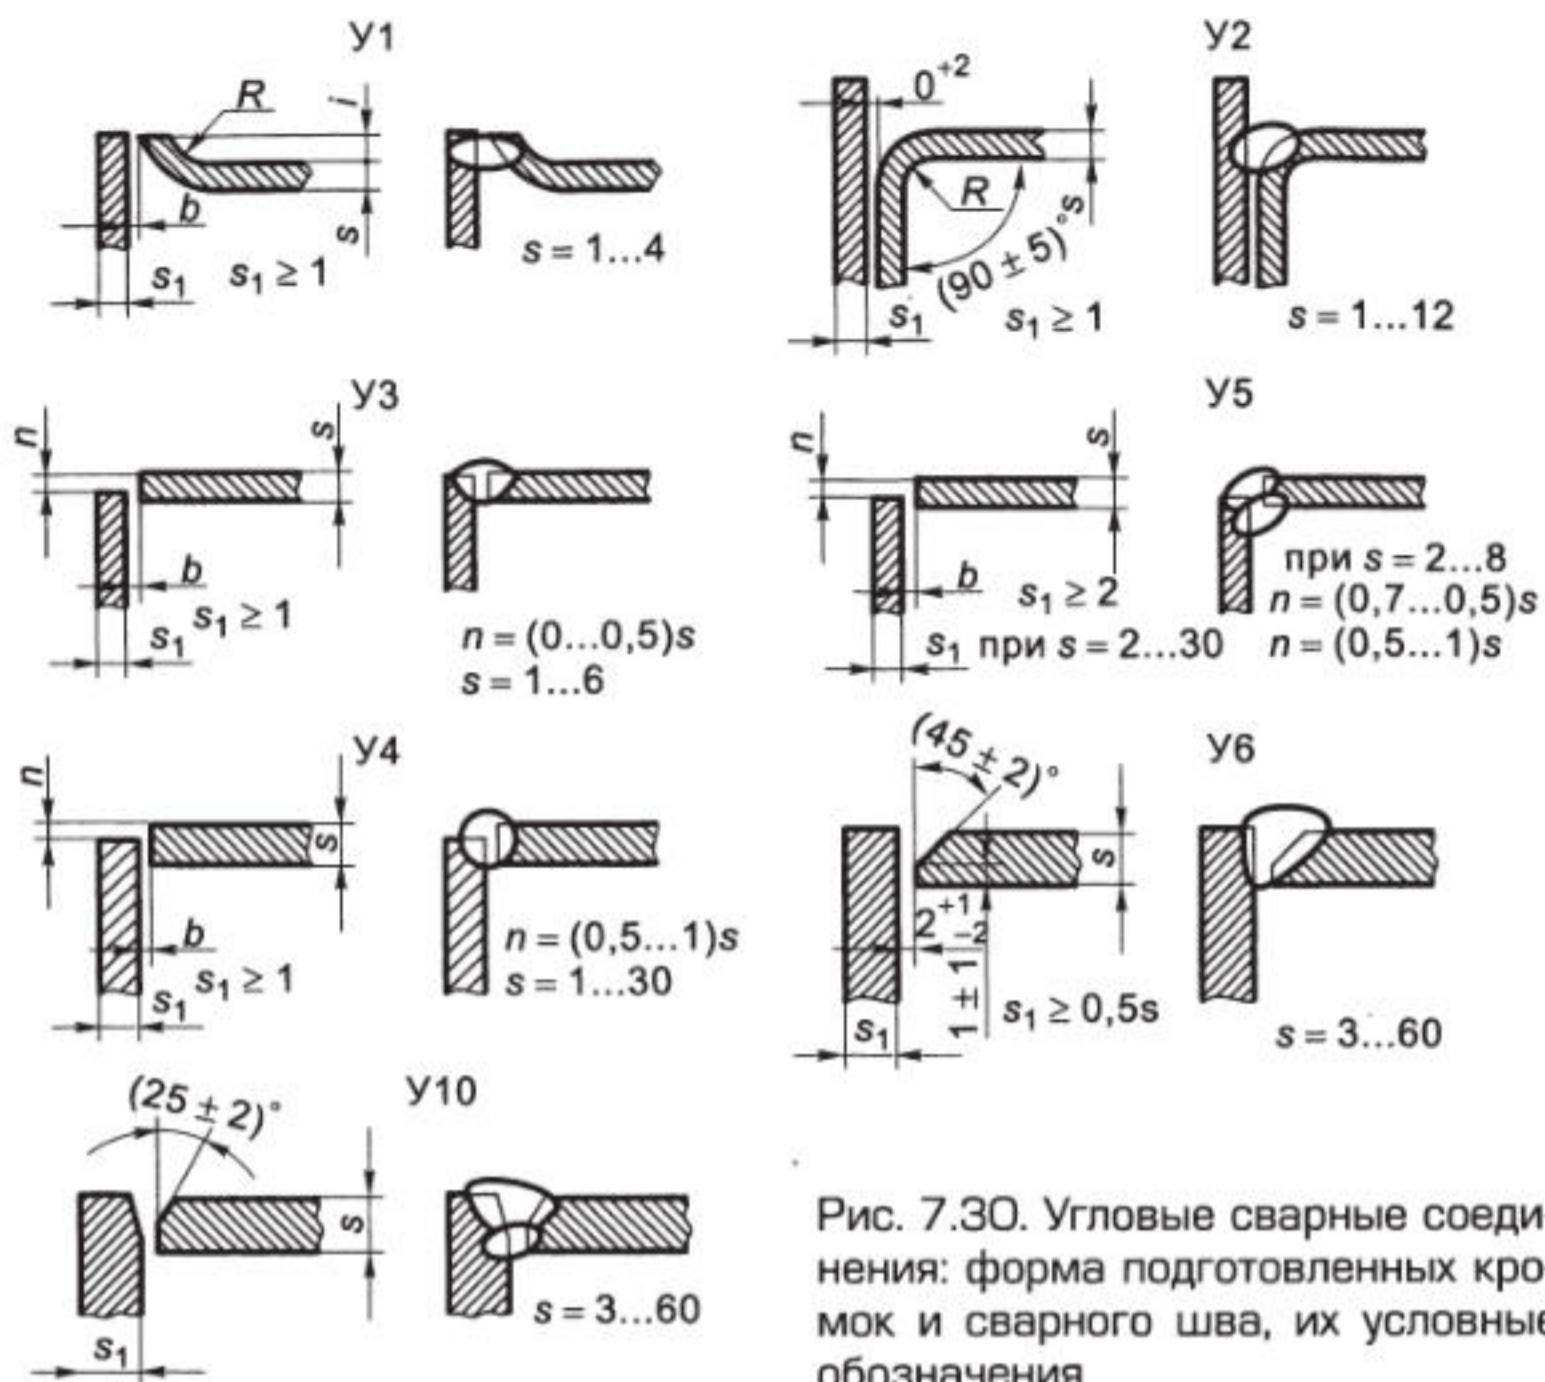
Угловые сварные соединения: форма подготовленных кромок и сварного шва, их условные обозначения
